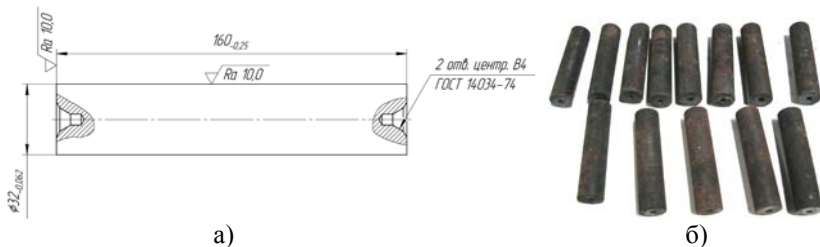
Конструктивна схема а) та партія заготовок зразків-виробів б)
